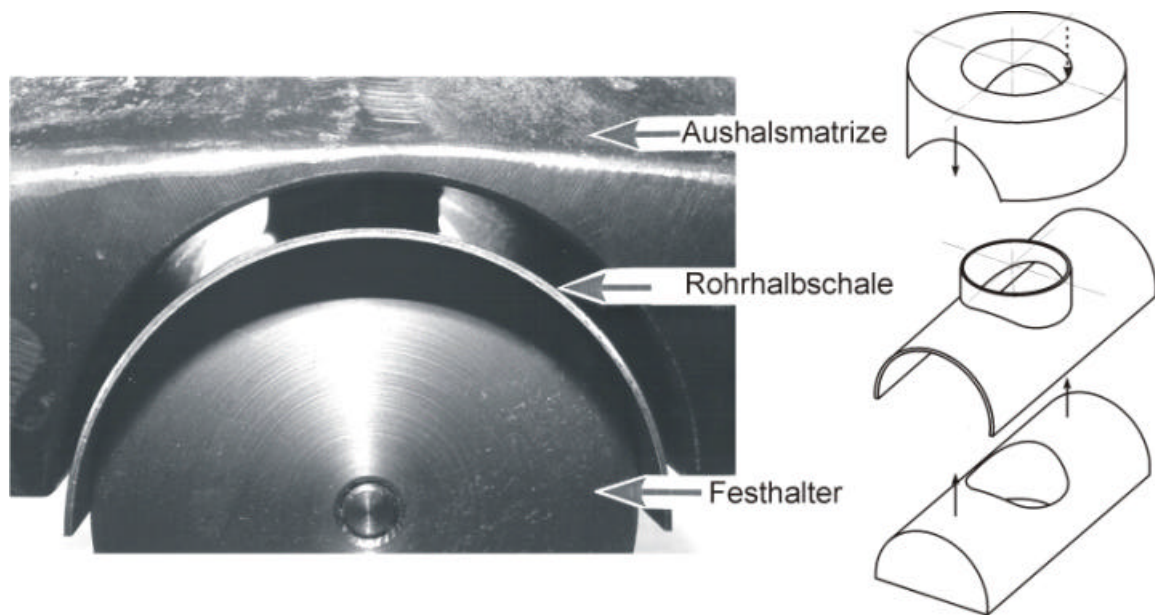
Werkzeugaufbau zum Aushalsen gewölbter Blechteile
